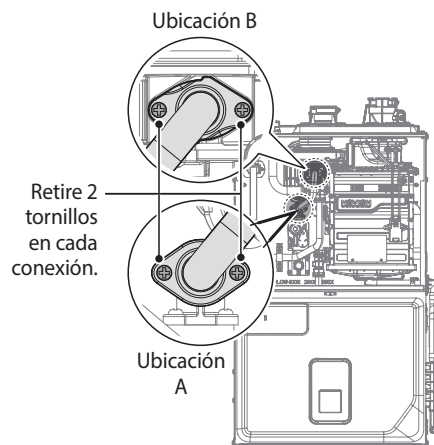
Desmontaje del adaptador de salida de la válvula de gas del conjunto de la válvula de gas y el motor del ventilador
